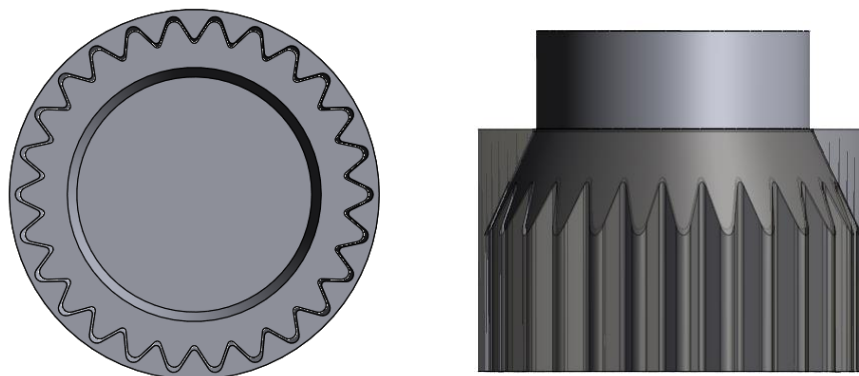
Imagen del CAD de la pieza 6 con el tercer tipo de soporte, en la que en la parte izquierda se puede comprobar la base del mismo que estaría en contacto con la cama de impresión y en la parte derecha la pieza 6 en la posición que se imprimiría con este soporte.
